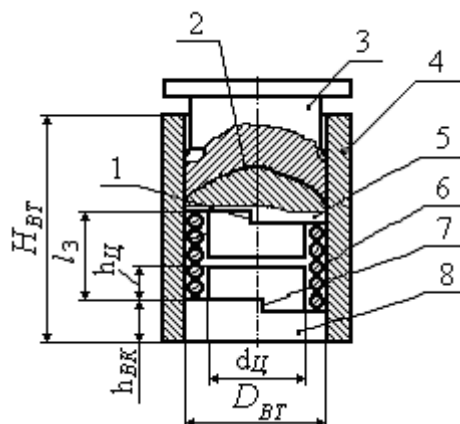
Основные детали и технологические размеры приспособлений для контактного заневоливания:
